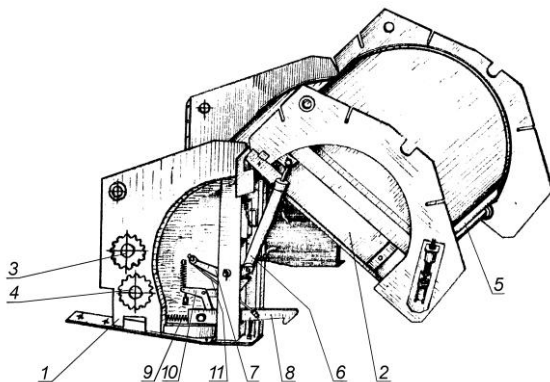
Камера прессования: 1 и 2 – передняя и задняя часть камеры; 3 – ведущий вал; 4 – верхний валец; 5 – ведомая ось прессующего механизма; 6 – гидроцилиндр; 7 – рычаг; 8 – защелка; 9 – пружина; 10 – рычаг; 11 – тяга.
